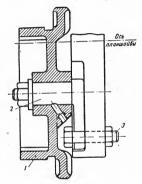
Схема установки на планшайбе токарного станка храповой муфты автомата:
